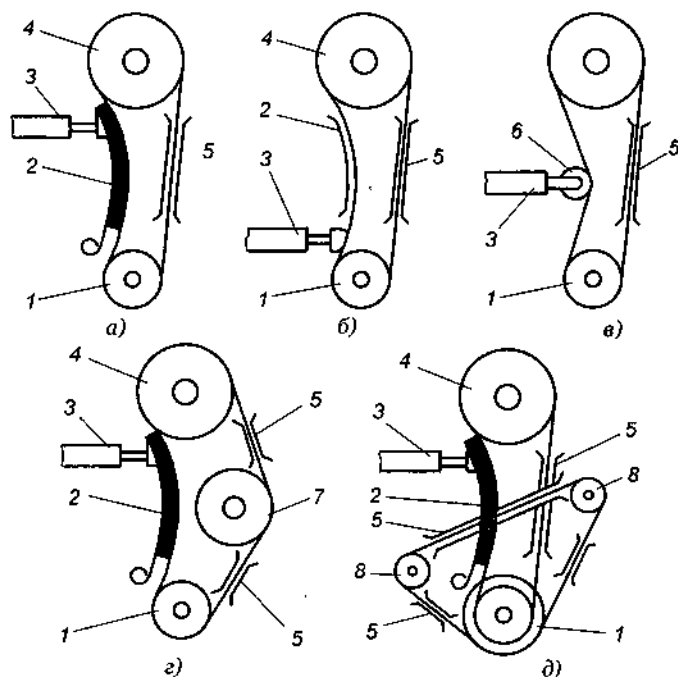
Различные конструкции приводов распределительного вала, в которых используются роликовые цепи: а — натяжение цепи с помощью башмака; б — натяжение цепи с помощью натяжителя; в — с помощью звездочки натяжителя; г — с промежуточным (вспомогательным) валом; д — с балансирными валами; 1 — звездочка коленчатого вала; 2 — башмак; 3 — натяжитель; 4 — звездочка распределительного вала; 5 — направляющие (успокоители); б — звездочка натяжителя; 7 — звездочка вспомогательного вала, 8 — звездочка балансирующего вала
